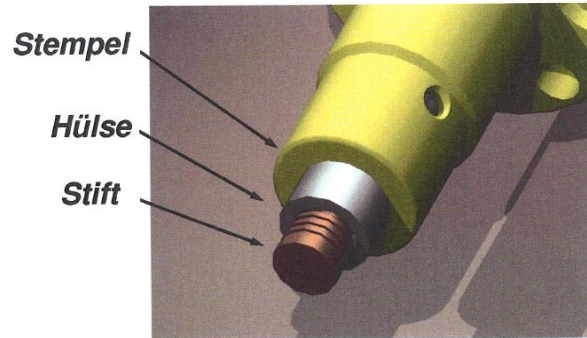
Schweißwerkzeug der Firma HARMS+WENDE [57]
